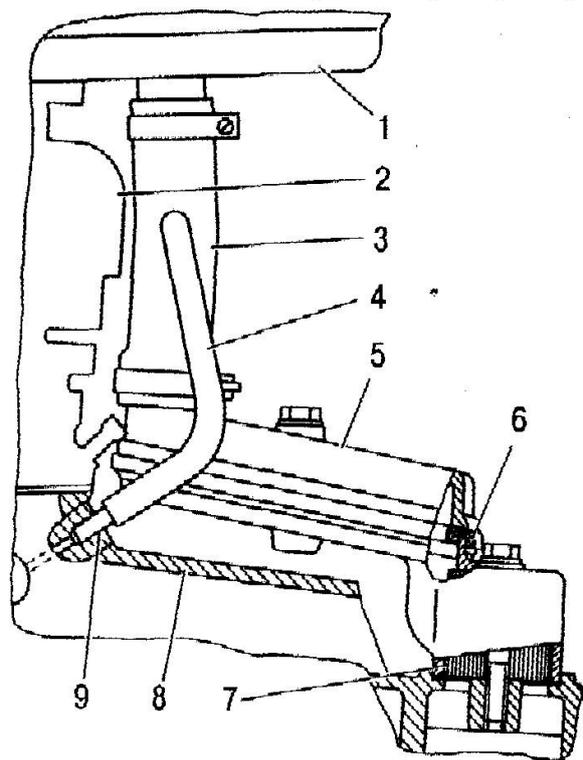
Схема закрытой системы вентиляции картера: 1 - воздушный фильтр; 2 - карбюратор; 3 - шланг основной ветви вентиляции; 4 - шланг дополнительной ветви вентиляции; 5 - маслоотделитель; 6 - прокладка; 7 - пламегаситель; 8 - впускная труба; 9 - штуцер
